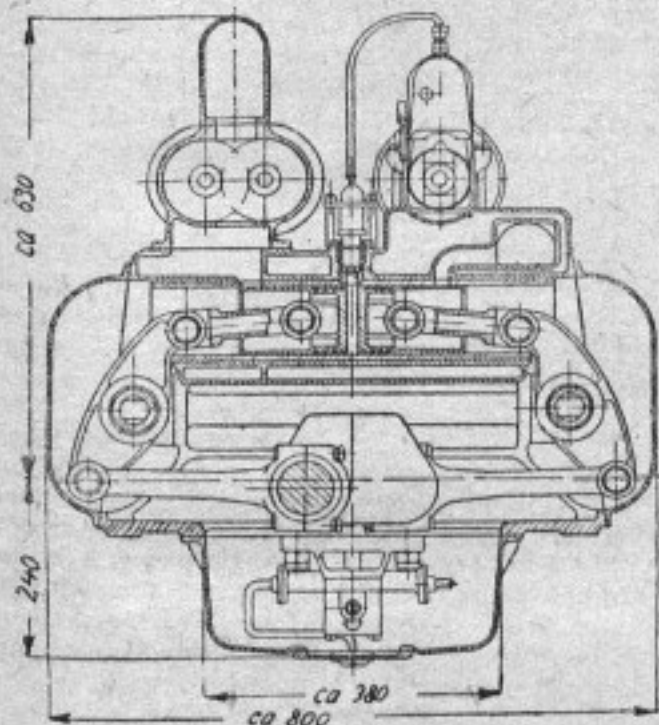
Двухтактный двигатель дизель ниж. Каппа
